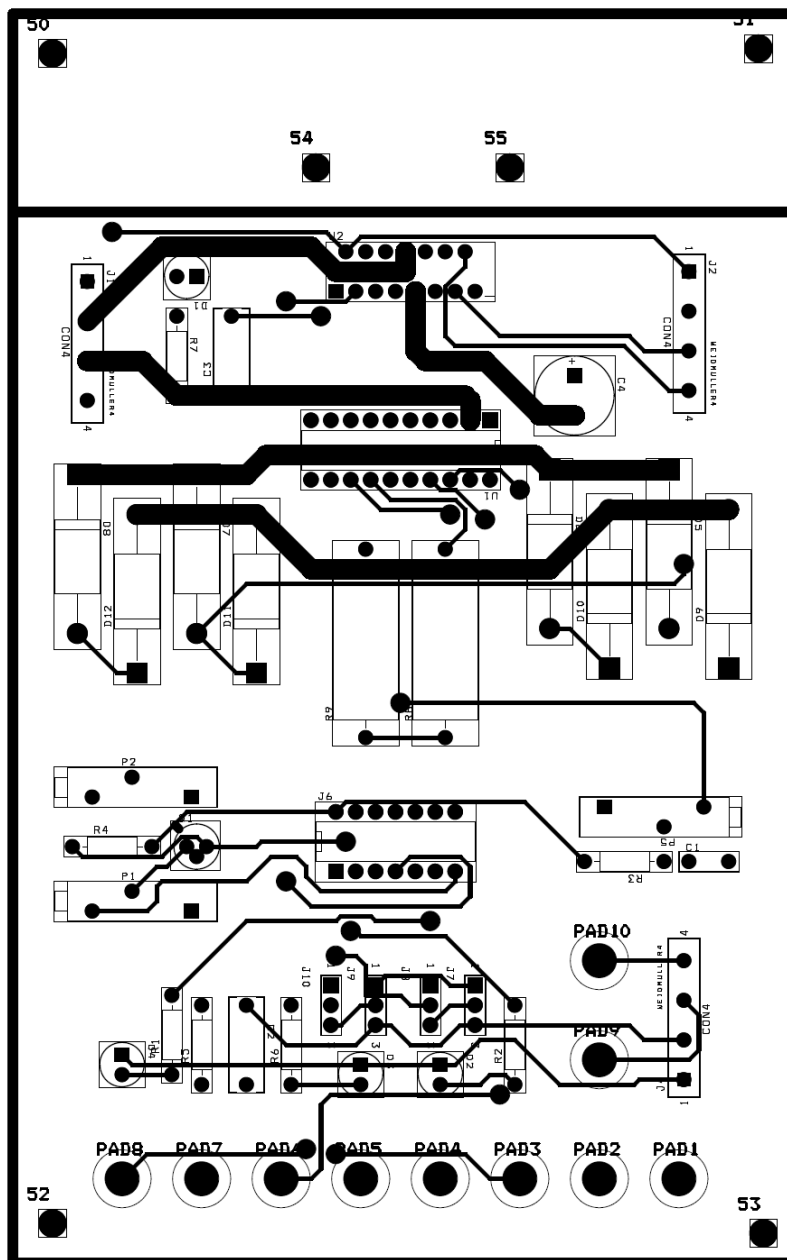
Capa superior (TOP) de la PCB de la interfície per al motor bipolar
